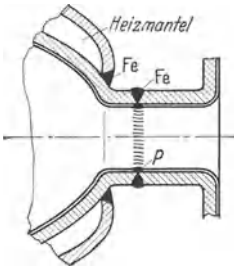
Anordnung der Schweißnähte an plattierten Behältern.
